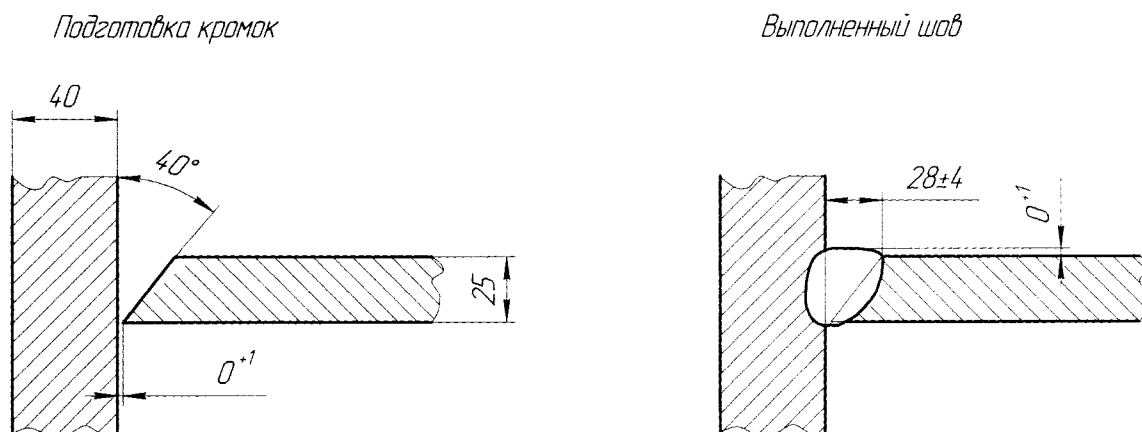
Эскиз сварного соединения перегородки со стенкой боковой
